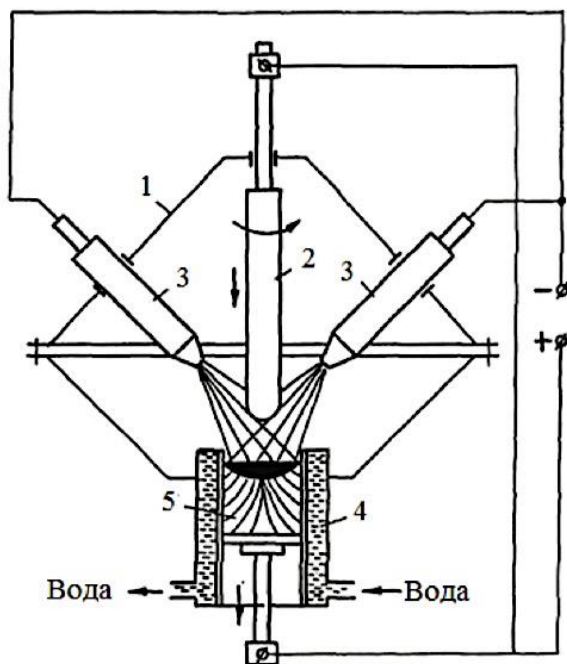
Схема установки плазменно-дугового переплава:
